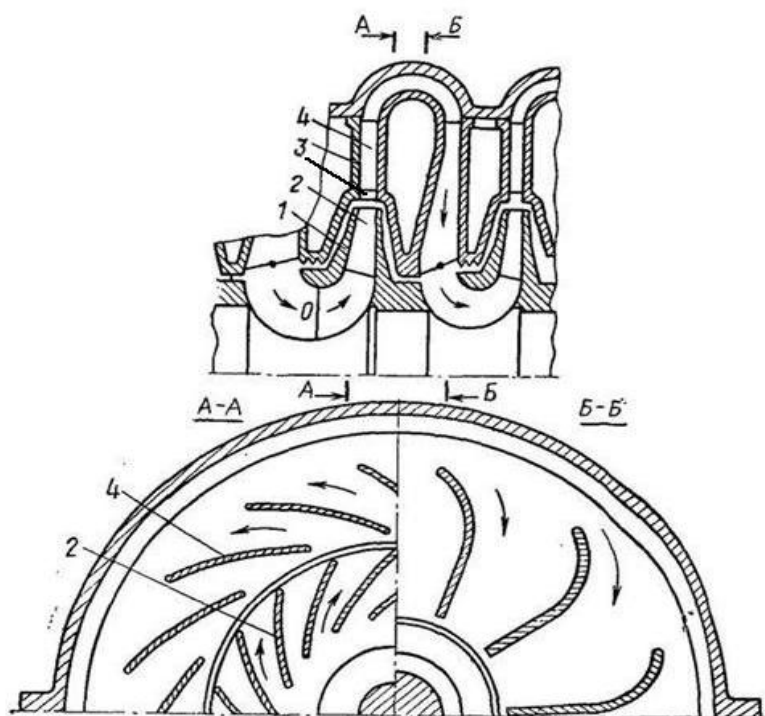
Схема промежуточной ступени центробежного компрессора:
